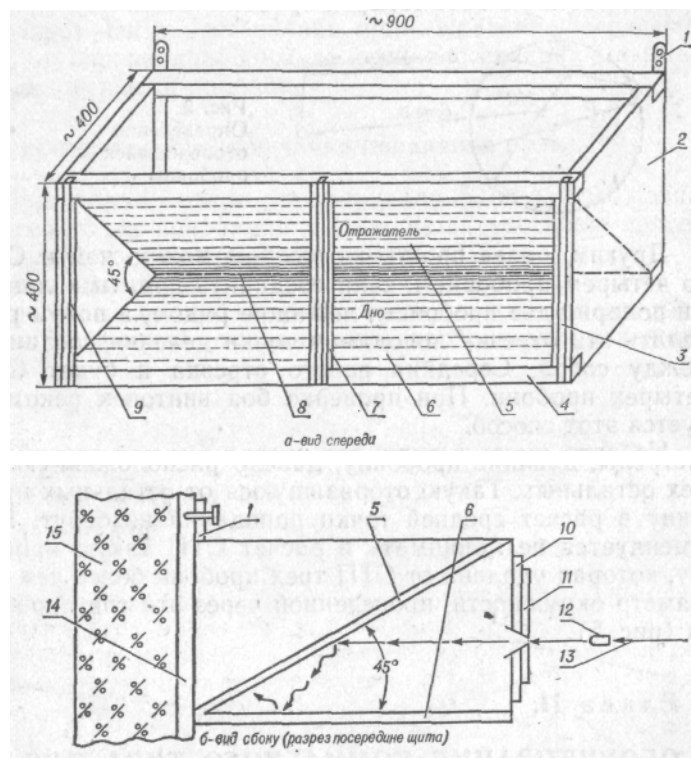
Двухщитовой пулеулавливатель для стрельбы из пневматических винтовок
